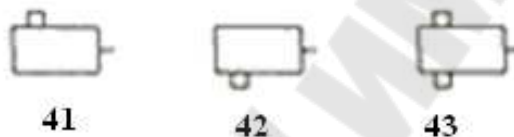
Варианты сборки коническо-цилиндрического редуктора
